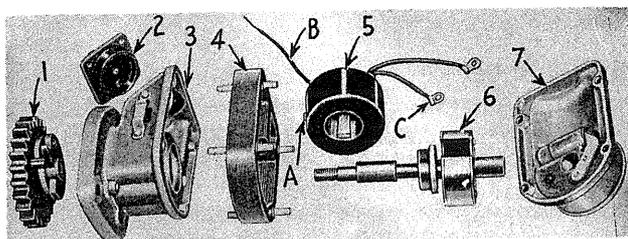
MAGNETO WICO TYPE "H" DONT ON A DEMONTÉ LA BOBINE. (IL N'EST PAS NECESSAIRE DE RETIRER LA COURONNE D'IMPULSEUR ET LE ROTOR COMME INDIQUE POUR DEMONTER LA BOBINE). 1 - IMPULSEUR. 2 - BORNE. 3 - BOÎTIER PRINCIPAL (EXTRÉMITÉ IMPULSEUR). 4 - NOYAU. 5 - BOBINE. 6 - ROTOR. 7 - BOÎTIER PRINCIPAL (EXTRÉMITÉ RUPTEUR).
